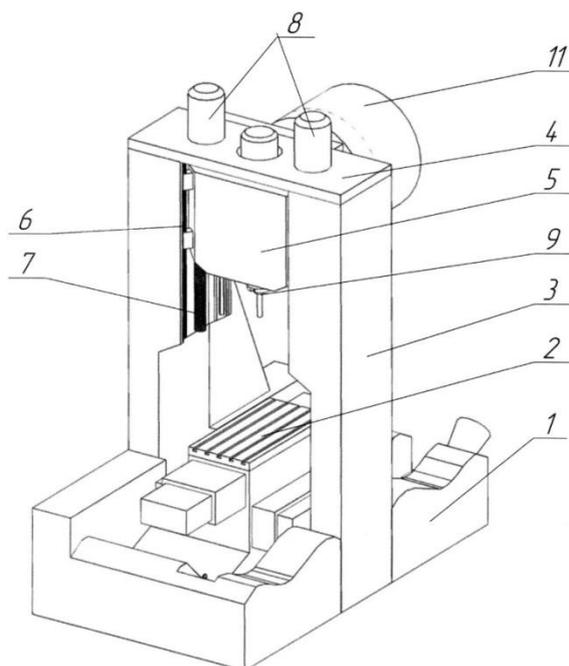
Чертеж вертикально – фрезерно – сверлильно – расточного станка с ЧПУ
